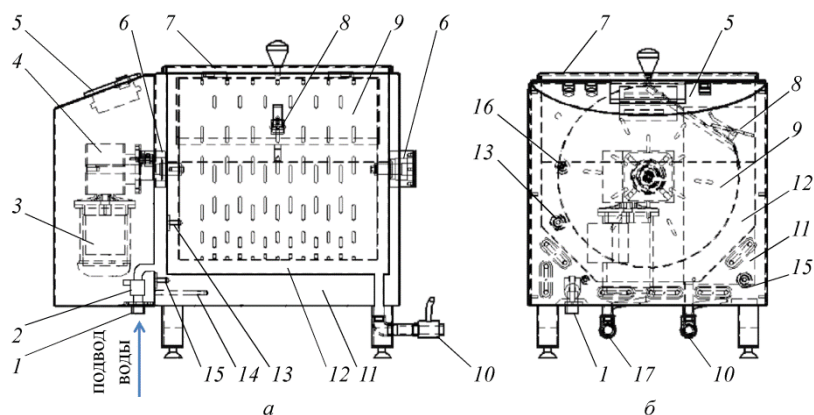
Устройство размораживателя молозива РМ-45 с вращающимся барабаном:
